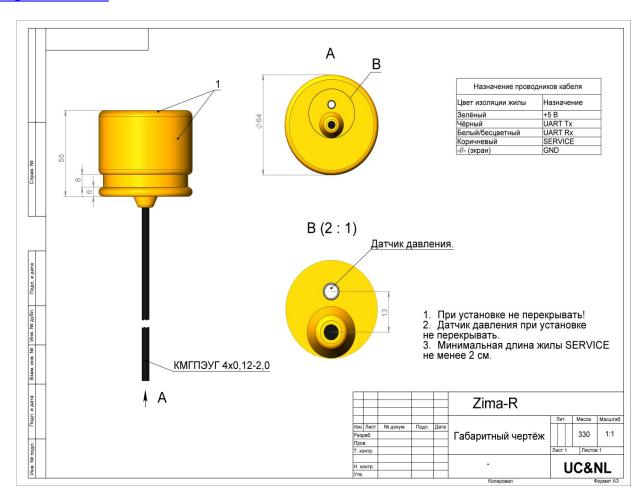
Габаритный чертеж маяка-ответчика ZimaR
